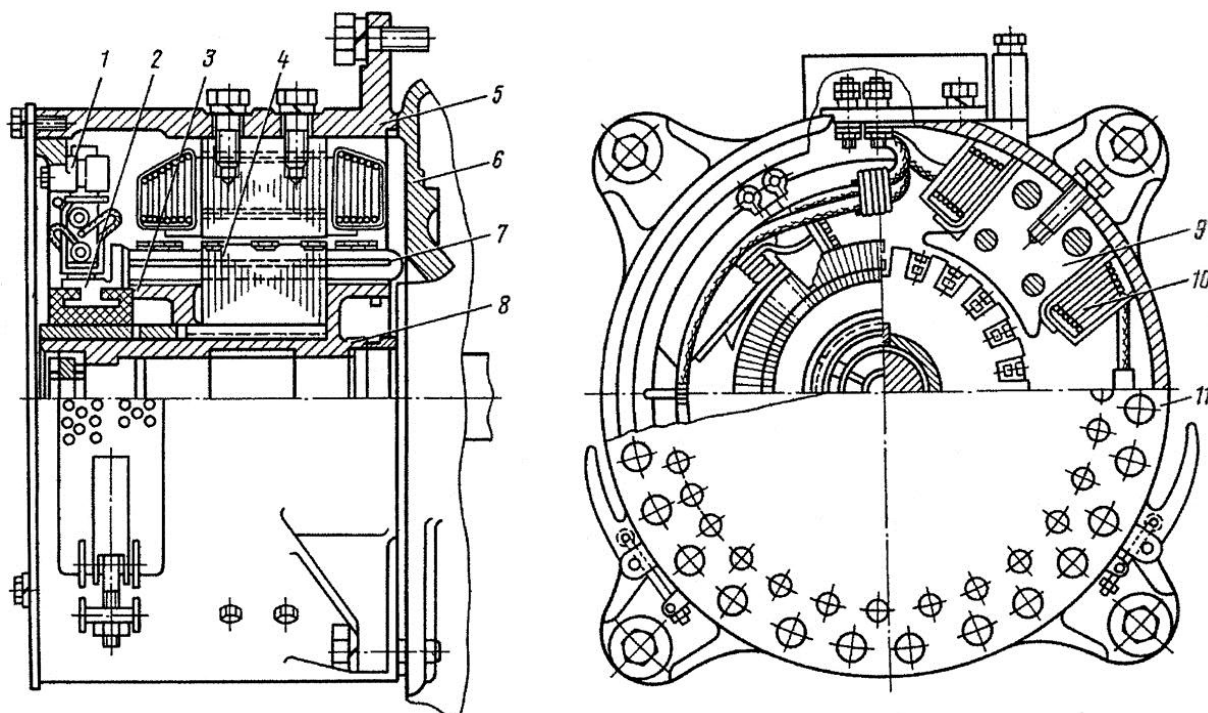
Продольный и поперечный разрезы генератора управления НБ-110В: 1 - щеточный аппарат; 2 - коллектор; 3 - нажимная шайба; 4 - сердечник якоря; 5 - остов; 6 - щит подшипниковый; 7 - обмотка якоря; 8 - втулка; 9, 10 - сердечник и катушка главного полюса; 11 - крышка
